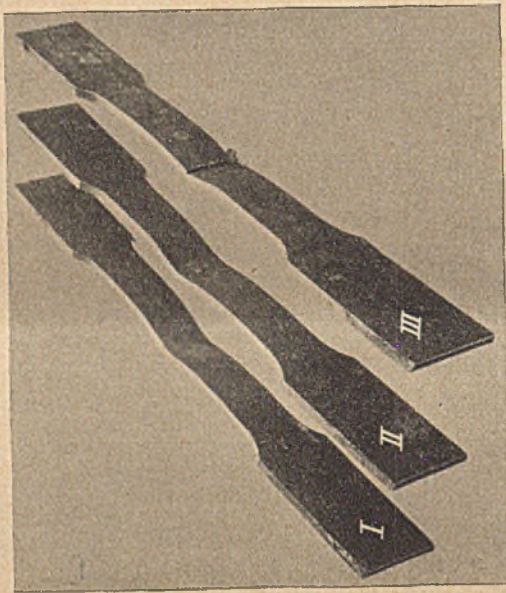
Stäbe mit Schweißnaht für die Zerreißproben.
